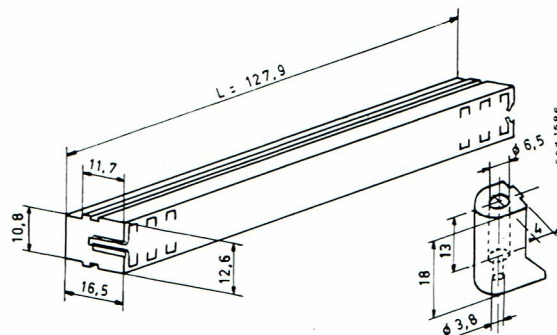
Dimensions du connecteur 2422.020.52592 et des pièces terminales 4322.026.11110
